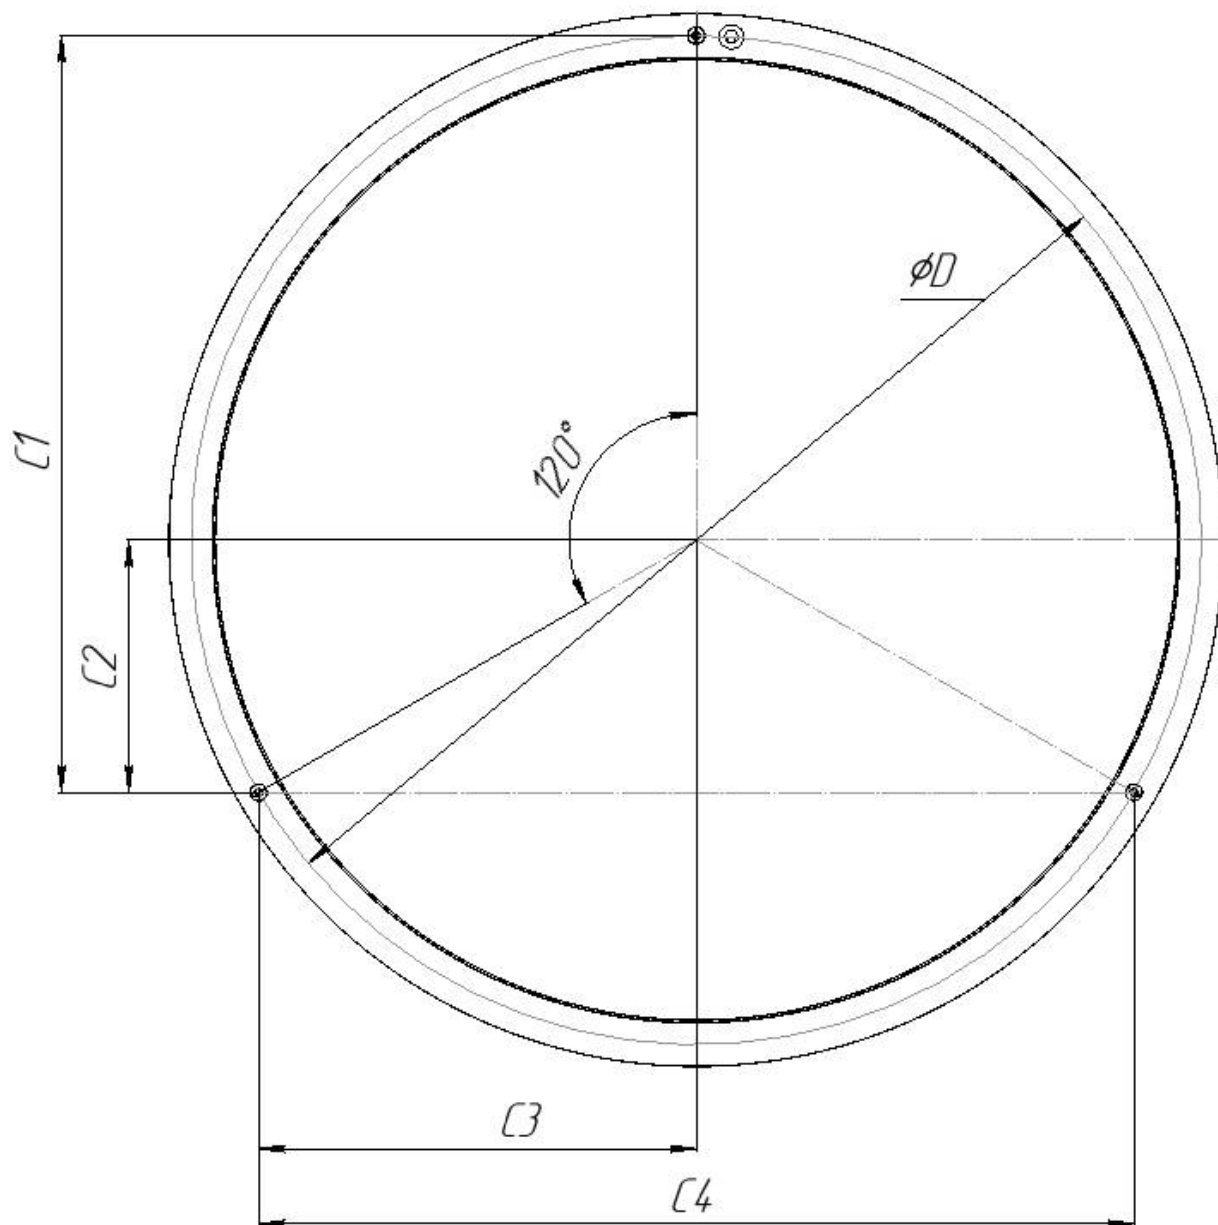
Схема разметки для монтажа тросовых захватов на опорную поверхность
